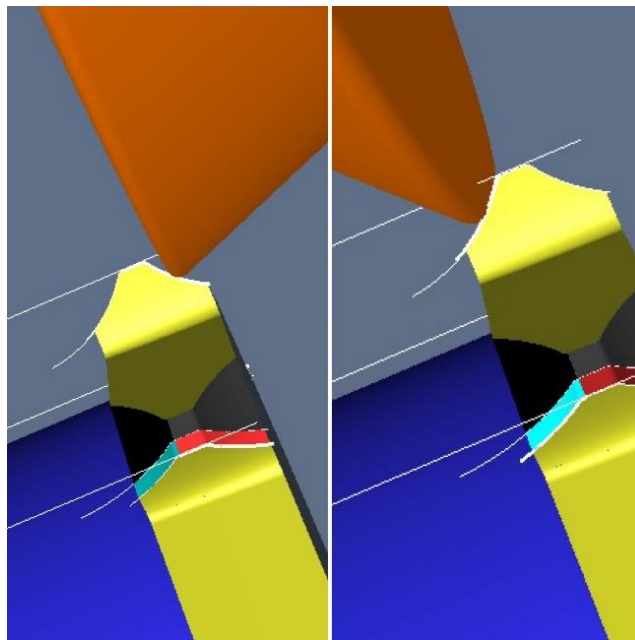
Kotoučová fréza po dokončení hrubovacích operací.
